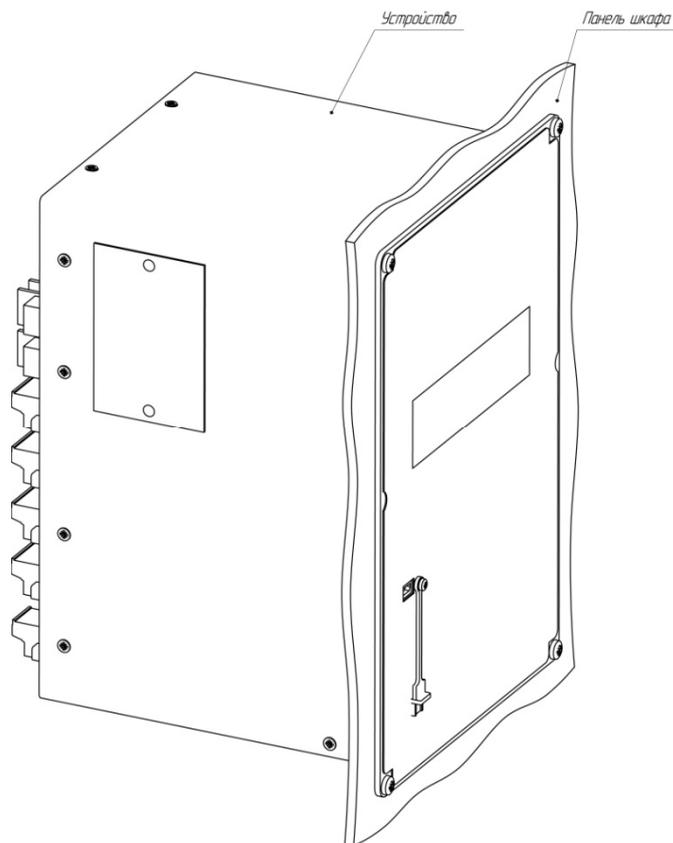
Габаритные и присоединительные размеры устройства РС83-ВС
